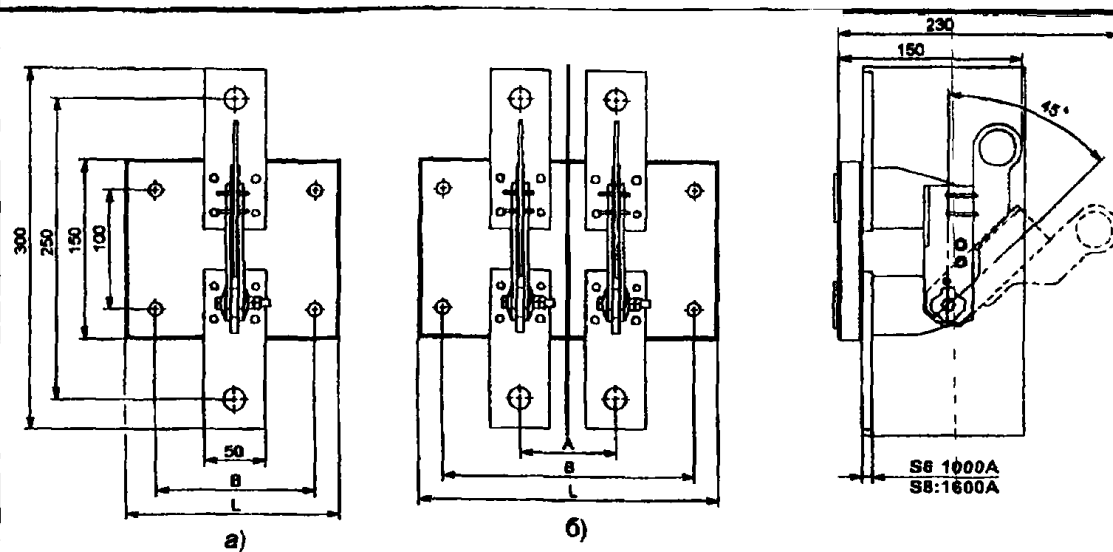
Разъединитель РЕ19 с рычагом для пополюсного оперирования штангой, заднего присоединения шин
